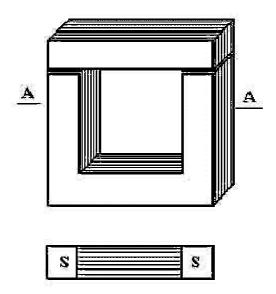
Vista y corte de un núcleo tipo apilado
